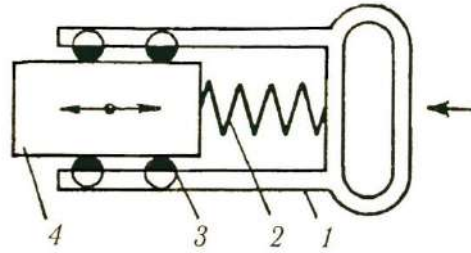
Схема віброізолювального держака: 1 – держак; 2 – пружний елемент; 3 – підшипник; 4 – корпус
